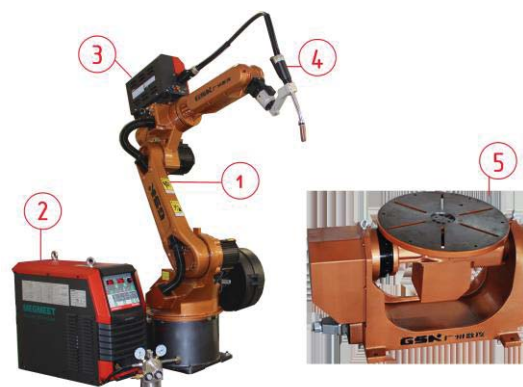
Составляющие промышленного сварочного робота: 1 – манипулятор, 2 - источник питания для выполнения сварочных работ, 3 - подающий механизм сварочной проволоки, 4 – сварочная горелка, 5 – сварочный позиционер
